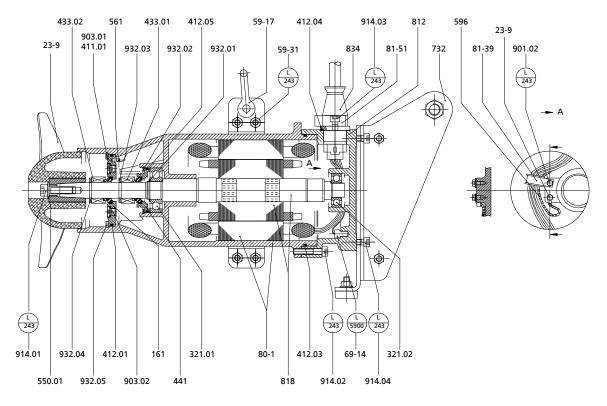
Чертеж общего вида Атматіх 200, материал корпуса двигателя – серый чугун
